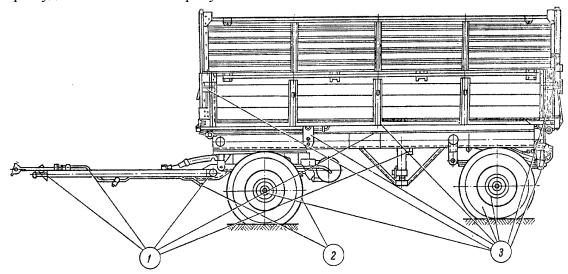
Схема консервации: 1— неокрашенные поверхности, шарнирные резьбовые соединения, оси бортов, пальцы опор, шины; 2— тормозные барабаны, трубопроводы; 3— шланги гидравлические, пневматические, принадлежности и инструменты
